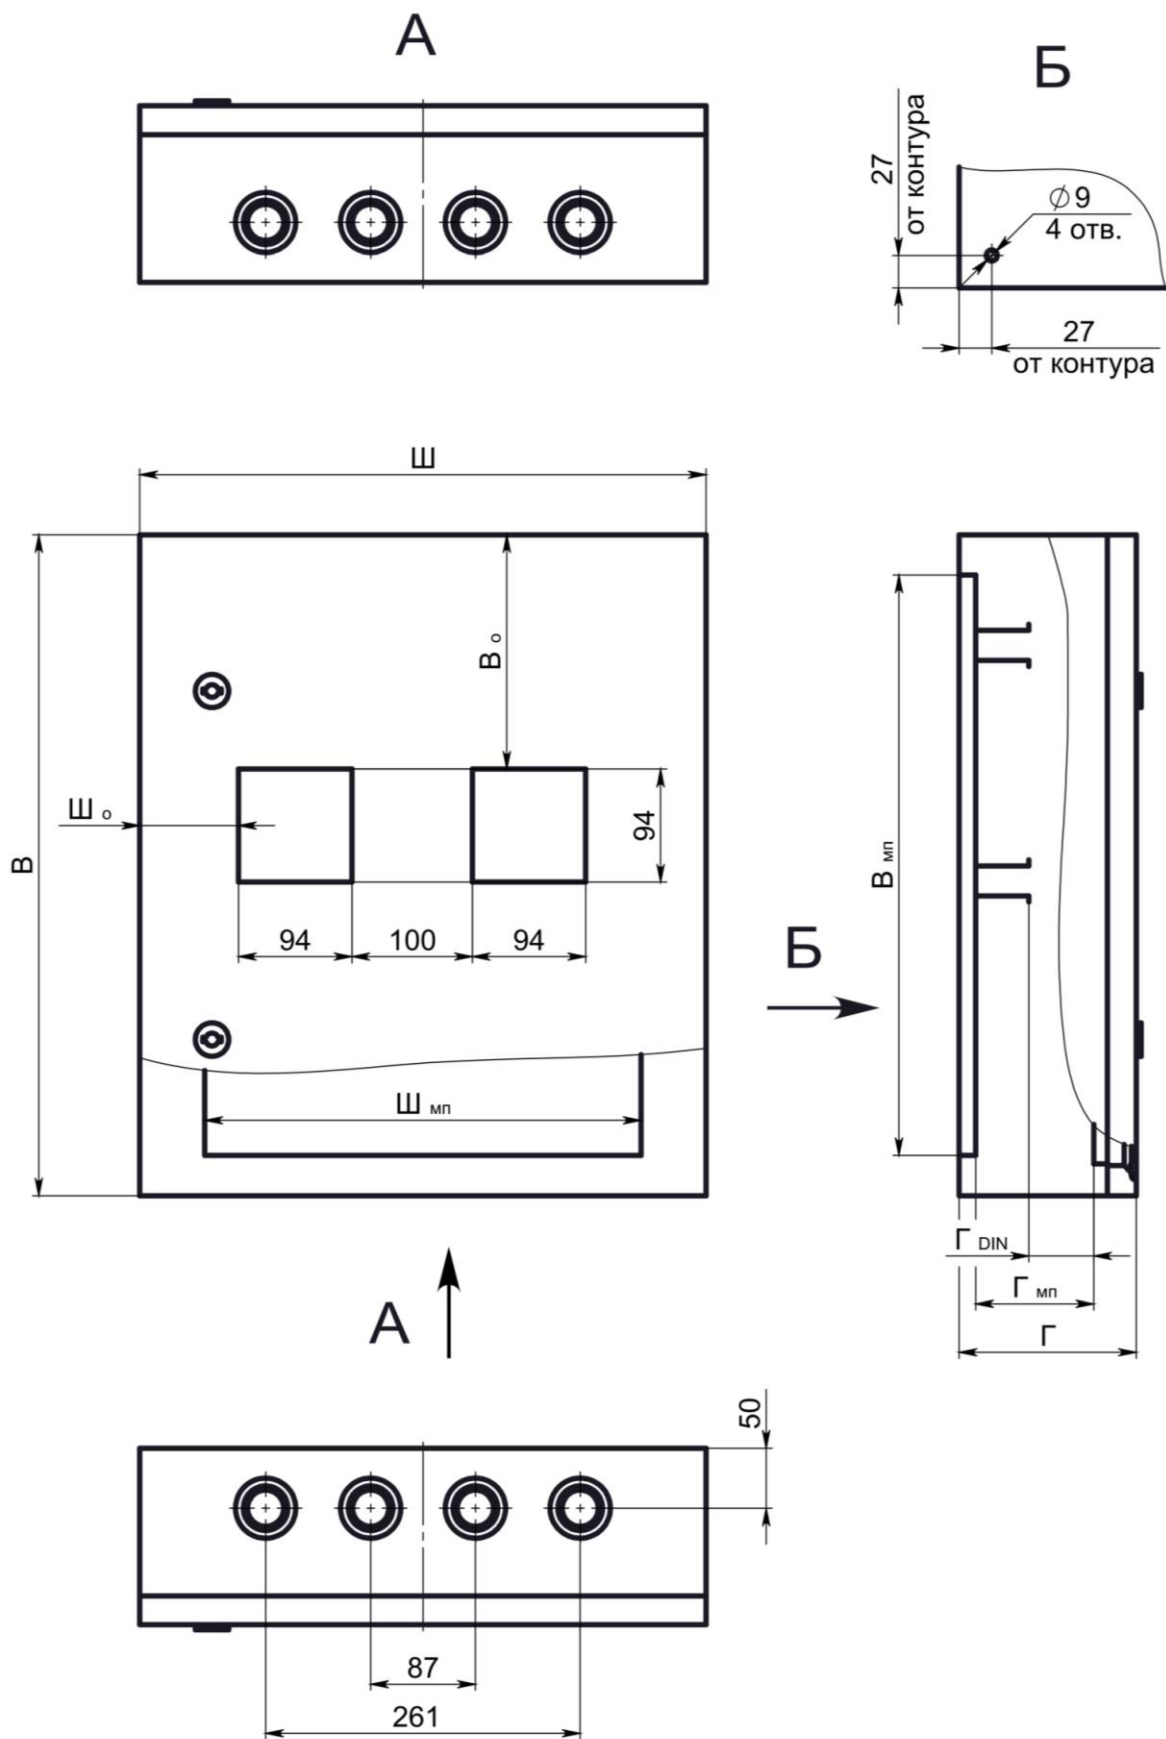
Габаритные, установочные и присоединительные размеры корпуса ЩУРН-ПРО-3х2-МП/18-550х470х147-IP66-УХЛ1 (код 367476)
